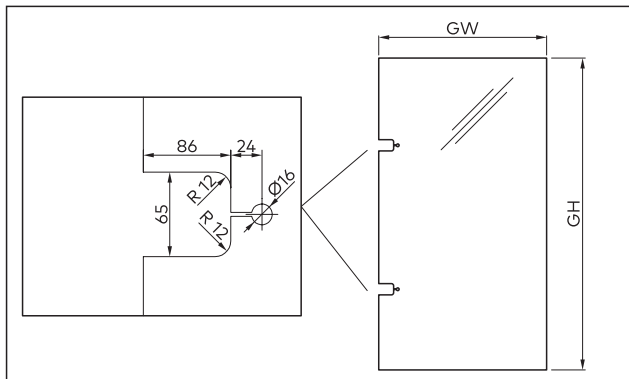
Glasbearbeitungen für die Wandbefestigung mit aufliegender Montageplatte
